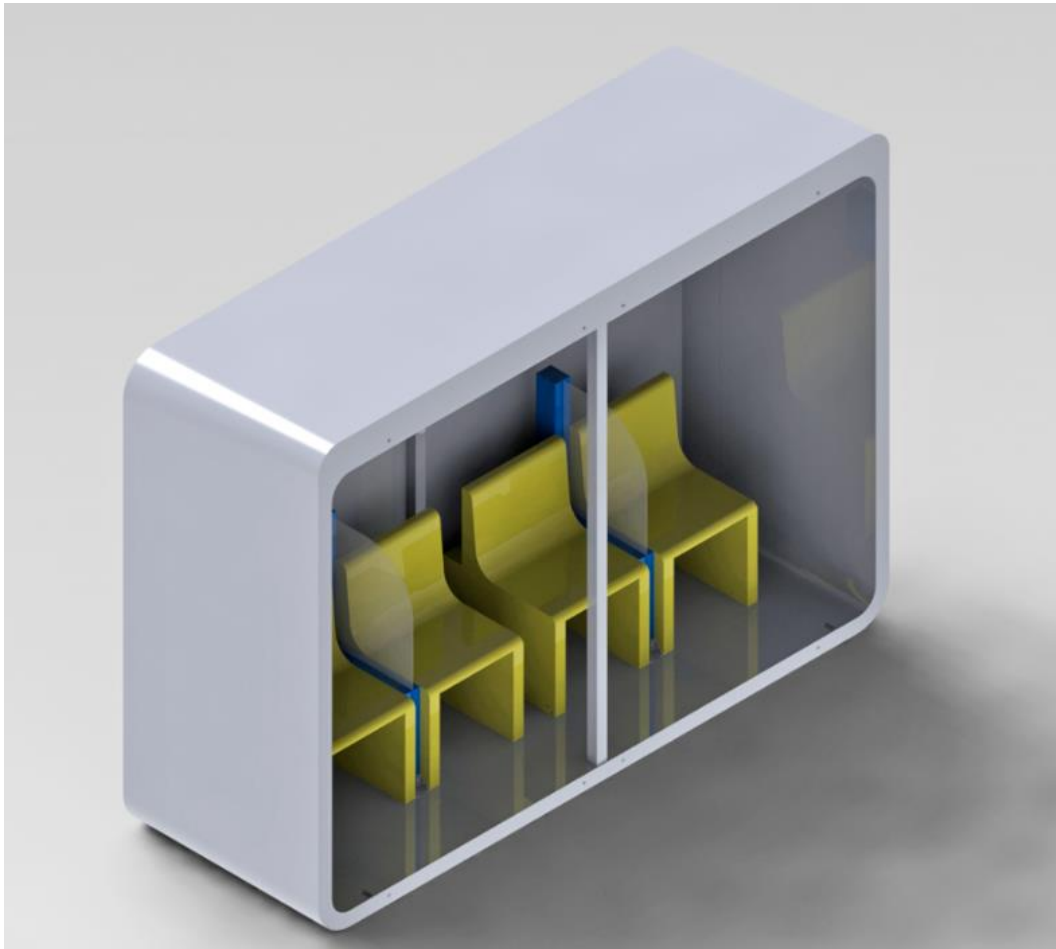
Ensamblaje conjunto. Montaje de 8 soportes de techo.
